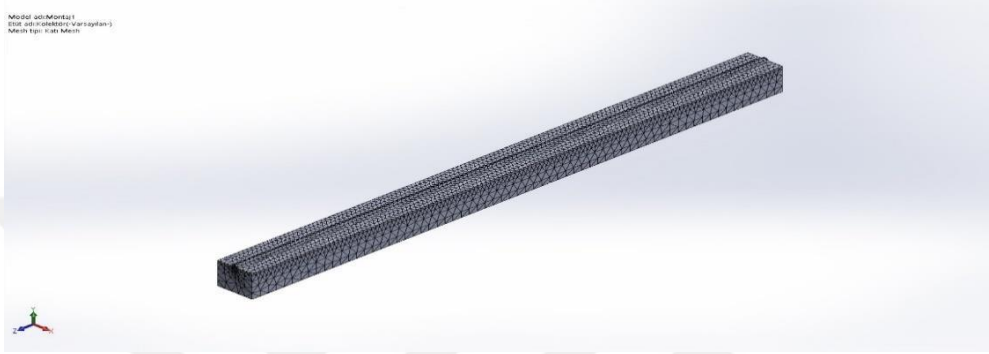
Tasarımı yapılan kollektör ön görünüşü
